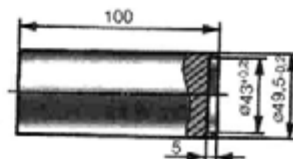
Оправка для выпрессовки резинометаллического шарнира из ушек рессор. Материал: сталь 40X, HRC 30–34
